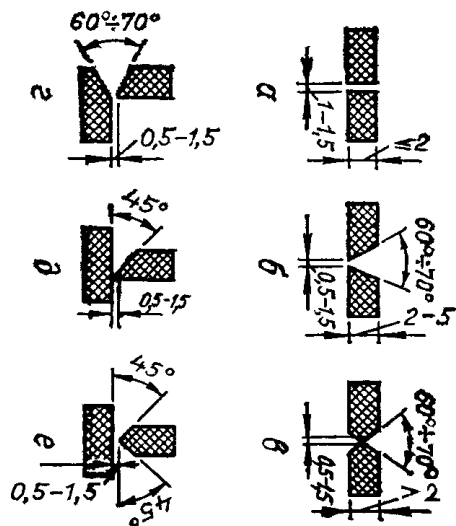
Подготовка кромок деталей перед сваркой горячим газом:
